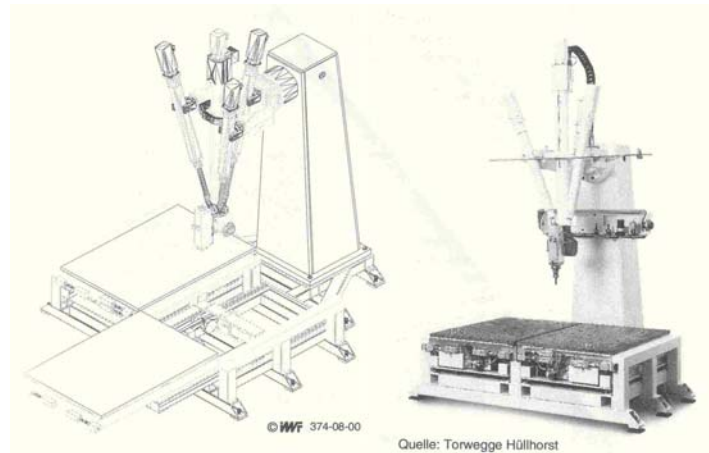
Tricept zur Holzbearbeitung [Hes00]
